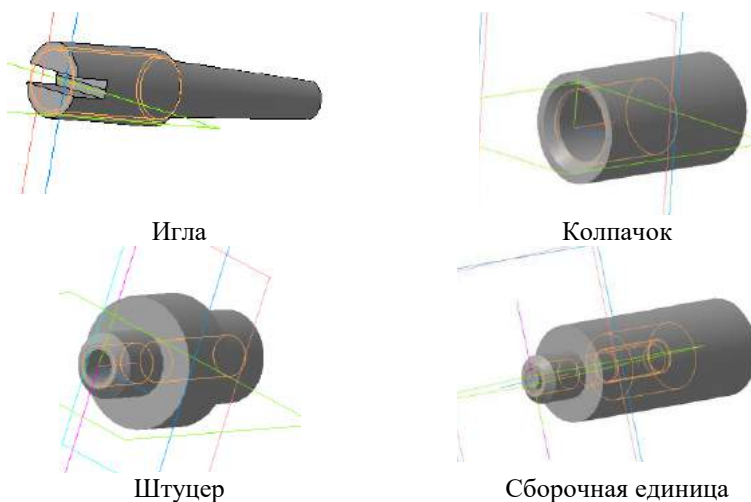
3-х мерное изображение деталей и сборочной единицы
